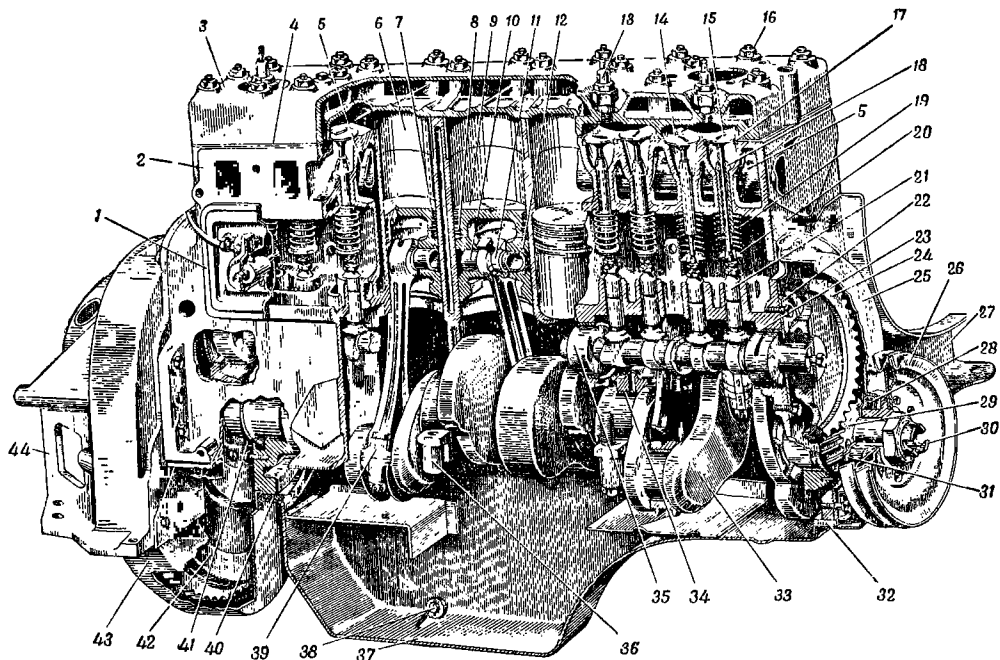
Двигатель ГАЗ-51 в разрезе.
